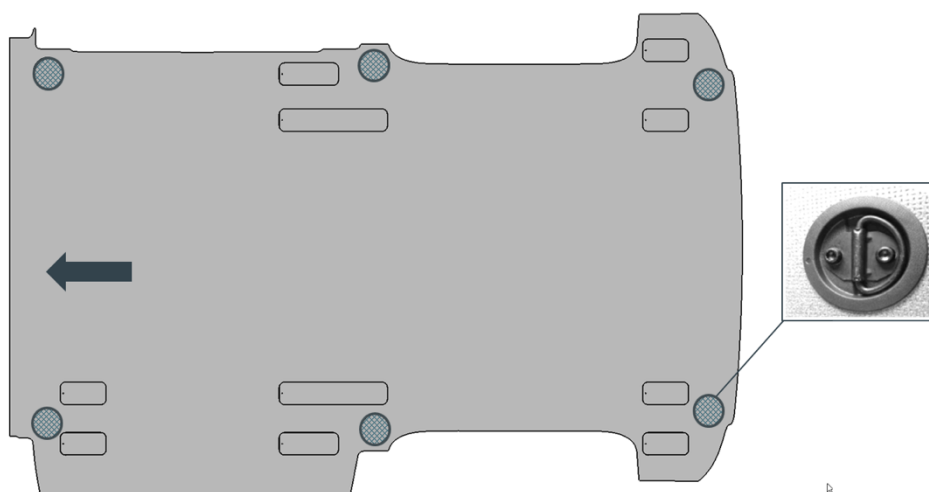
plancher universel (5BM)-points de fixation en forme de coupelle aux points d'arrimage
